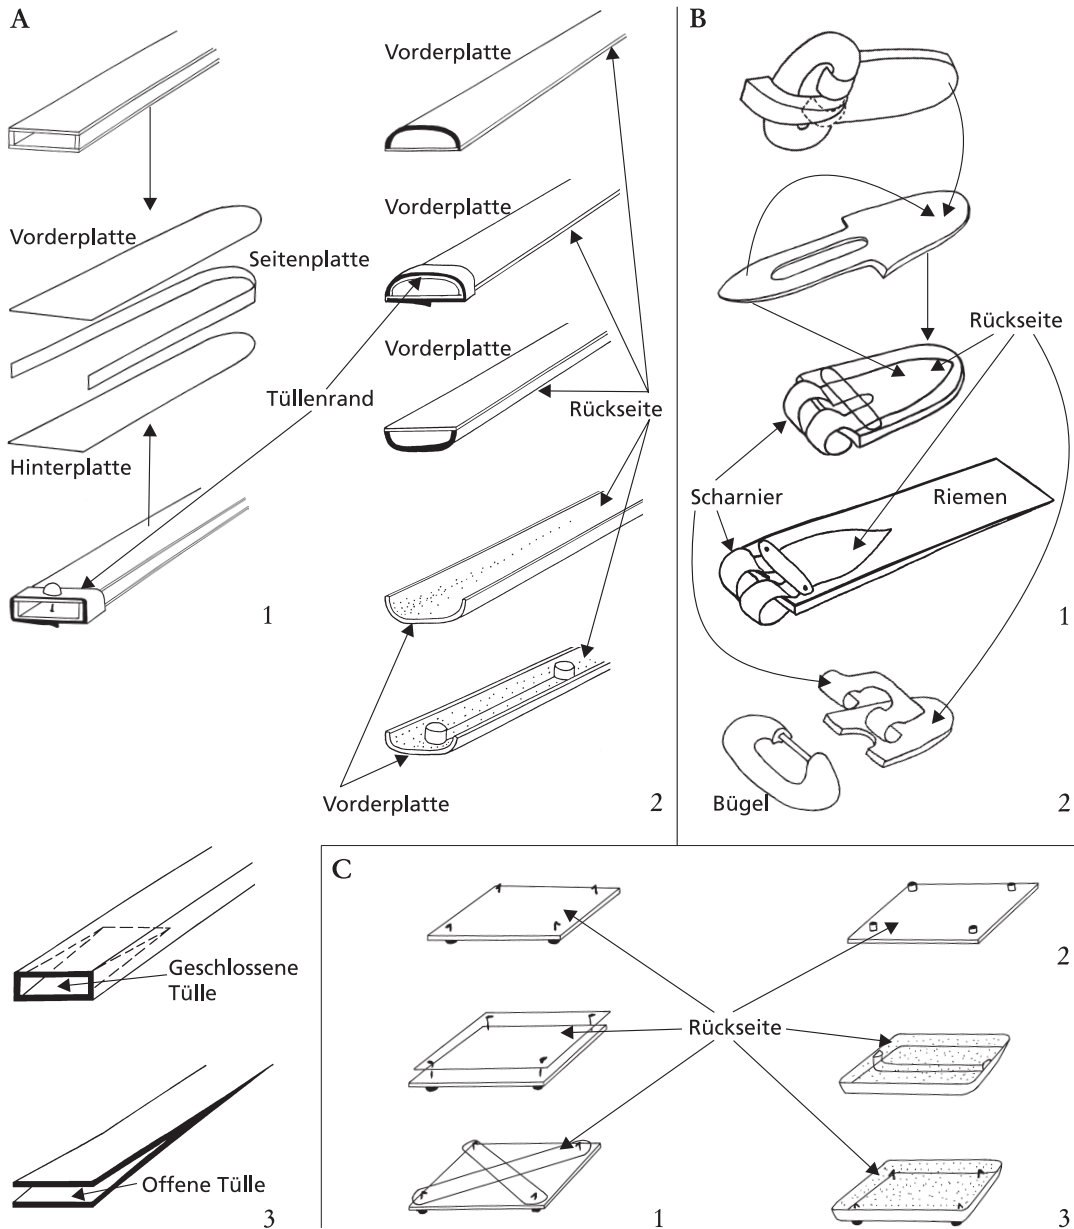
Konstruktionszeichnungen: A1 Konstruktion einer dreiteiligen Riemenzunge, A2-3 Konstruktionsvarianten der zweiteiligen Riemenzungen; B1-2 Konstruktionsvarianten von Schnallen mit innerer Lasche; C1 Montagevarianten von Beschlägen mit durchgeschlagenen Nieten, C2 Montage von Beschlägen mit angelöteten Nieten; C3 Montagevarianten von Beschlägen mit Bleifüllung. – M. 1 : 2.
